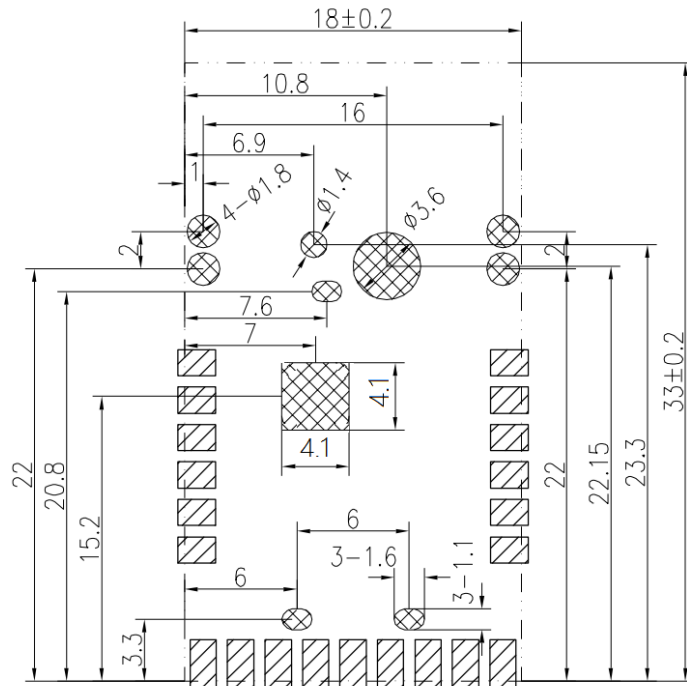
邮票孔封装尺寸 (安装焊盘, 单位: mm)
